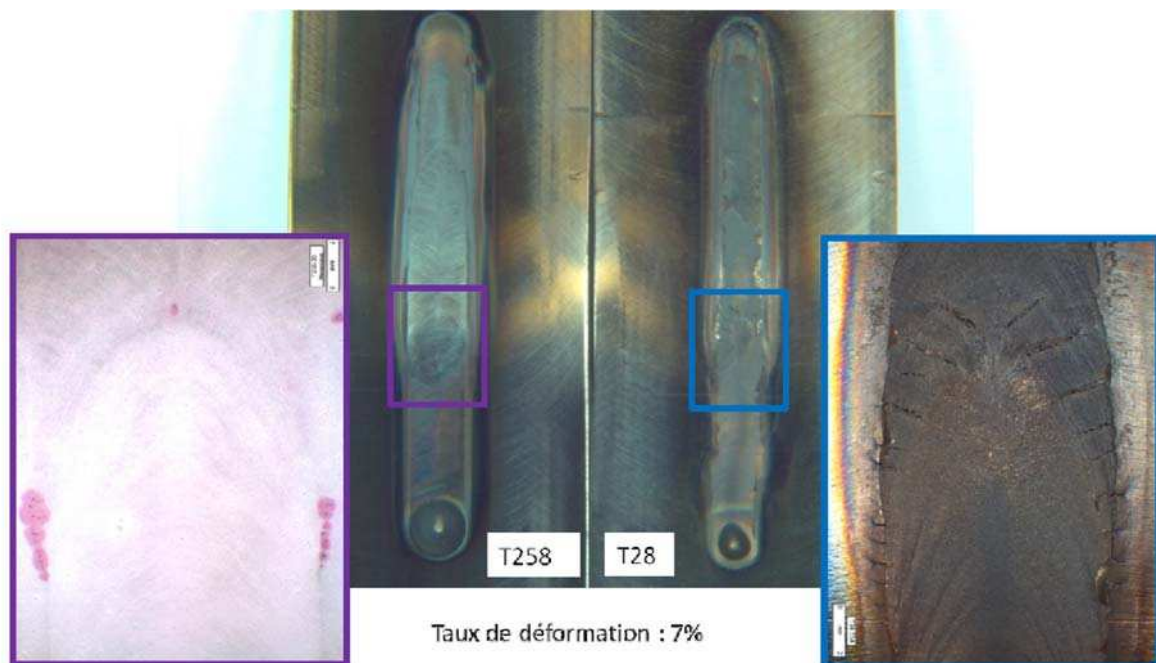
Fissuration à chaud après essai Varestreint [8]
